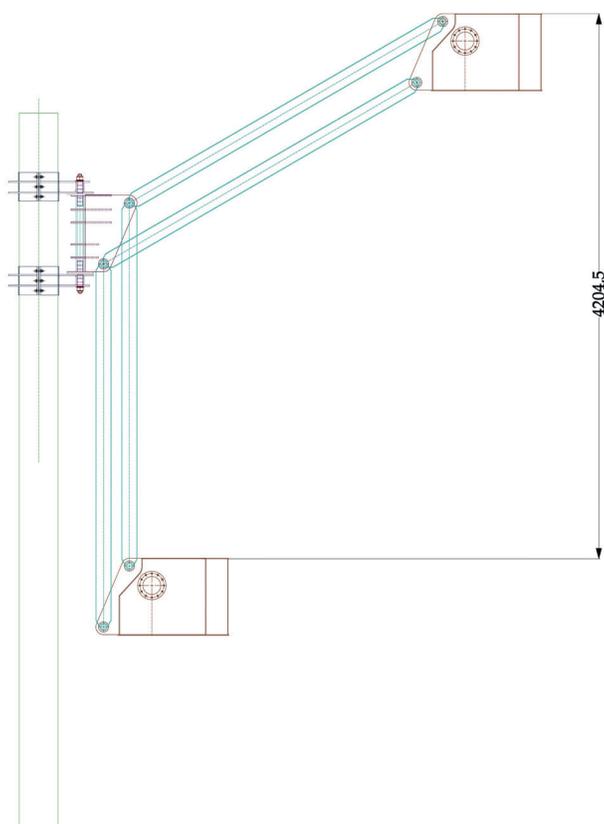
Vista laterale dell'installazione (misura espressa in mm)
